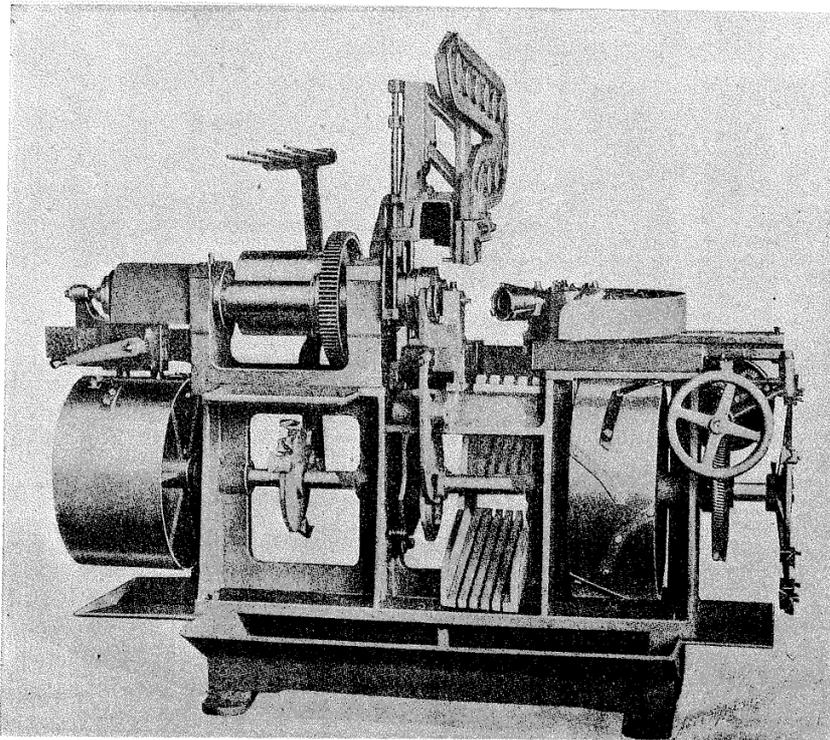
Décoleteuse automatique Pratt-Whitney avec magasin Couch pour volants de machines à coudre. Les pièces brutes de fonte sont placées dans le magasin, et le travail s'opère automatiquement jusqu'à achèvement complet; ce travail comprend le tournage de la jante, le façonnage des deux côtés du moyeu, le perçage et l'alésage du moyeu, etc. Cette série d'opérations comprend la prise de la pièce brute dans le magasin, son placement dans le mandrin, le finissage, l'enlèvement de la roue du mandrin et son rejet dans une boîte. Le total de temps requis est de quatre minutes et demie, ce qui donne une moyenne de 120 volants toutes les dix heures. Un seul homme aidé d'un gamin suffit pour veiller au travail d'une douzaine de ces machines. (Pour une description détaillée, voir *Revue de Mécanique*, mai 1900, p. 649.)
